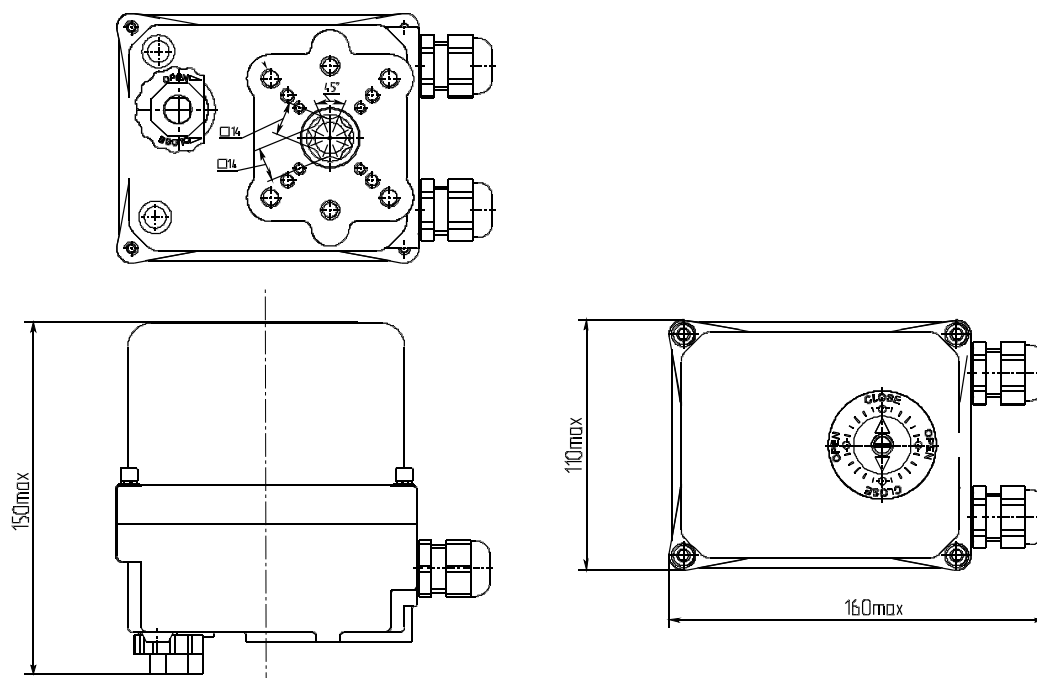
Габаритные и присоединительные размеры КСАТО 6 НЗМ 52/20-0,25
